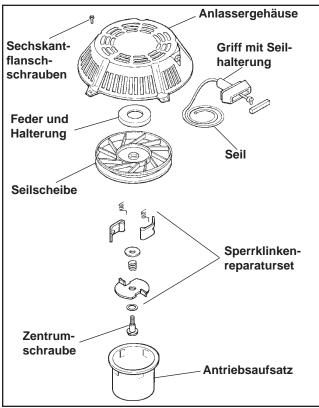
Seilzuganlasser - Explosionszeichnung.
